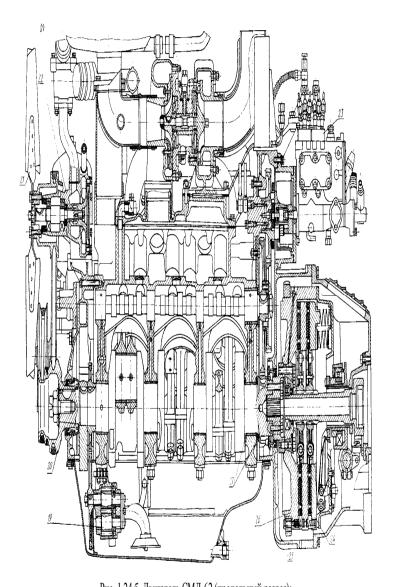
б. Двигатель СМД-62 (продольный разрез): 19 – масляный насос; 20 – шкив коленчатого вала; 21 – вентилятор; 22 – водяной насос; 23 – топливный насос; 24 – муфта сцепления; 25 – картер маховика; 26 – маховик; 27 – полукольца упорные
